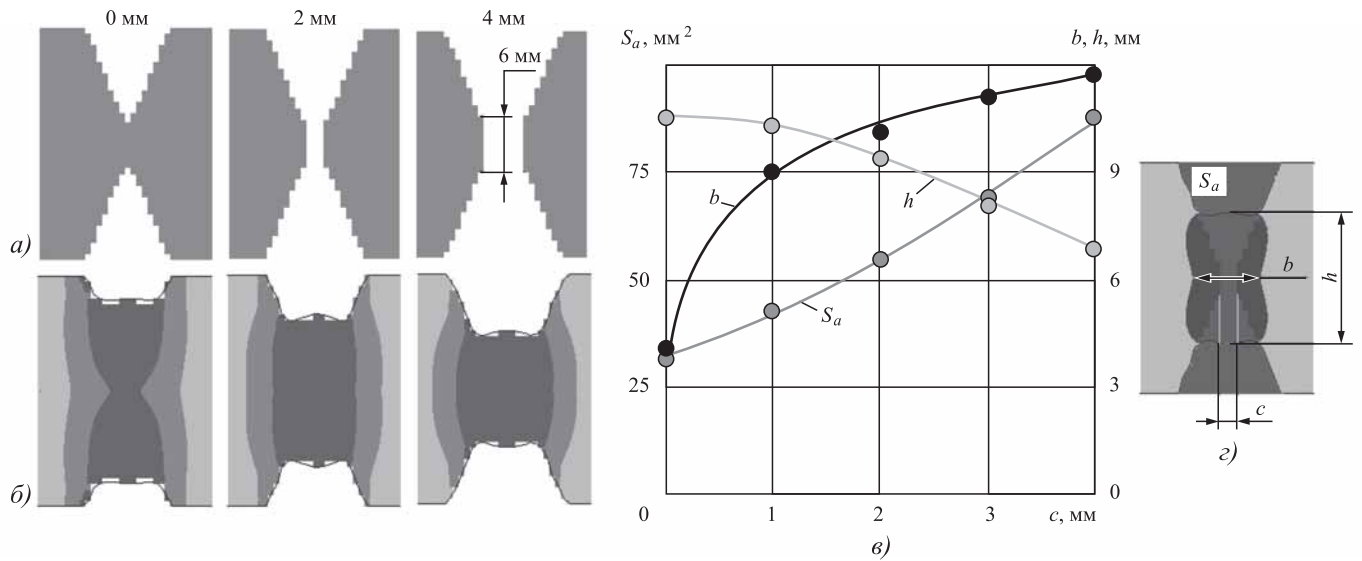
Влияние сборочного зазора на формирование корня шва:
